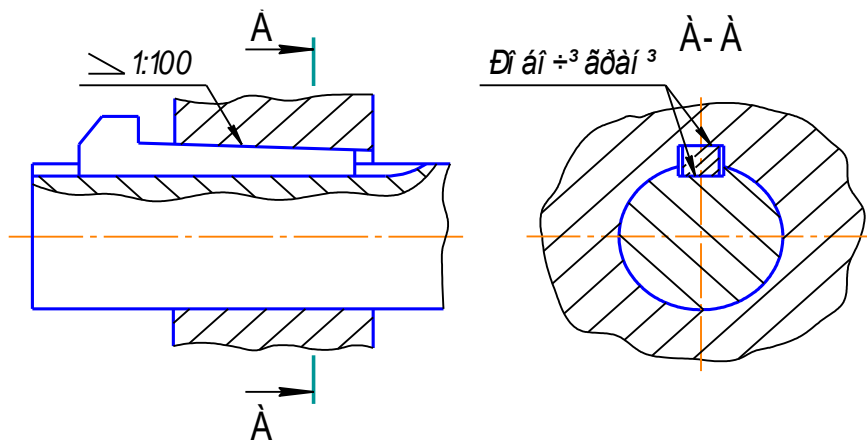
Конструкція шпонкового з'єднання з клиновою шпонкою
